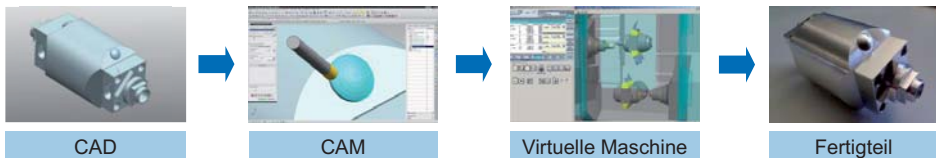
CAD-CAM-CNC-Kette mit Virtueller Maschine
